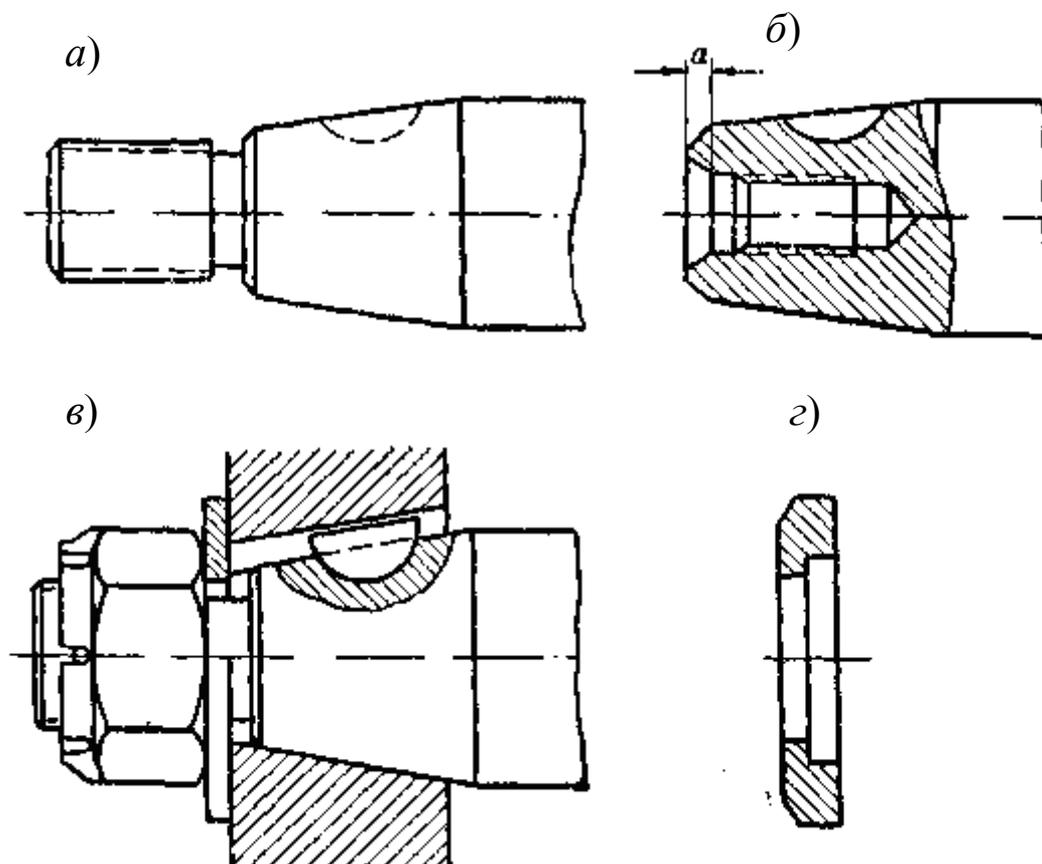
Конструкция переднего конца шпинделя шлифовального станка
